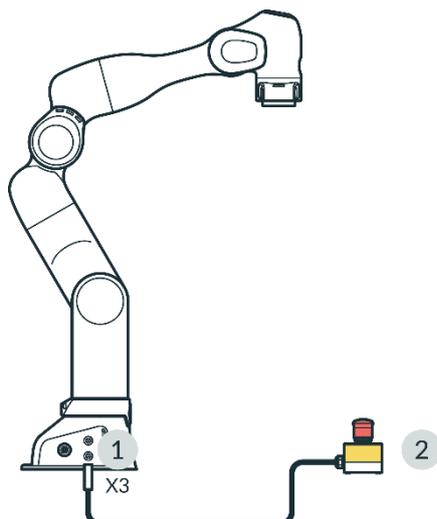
Collegamento del dispositivo di arresto di emergenza
